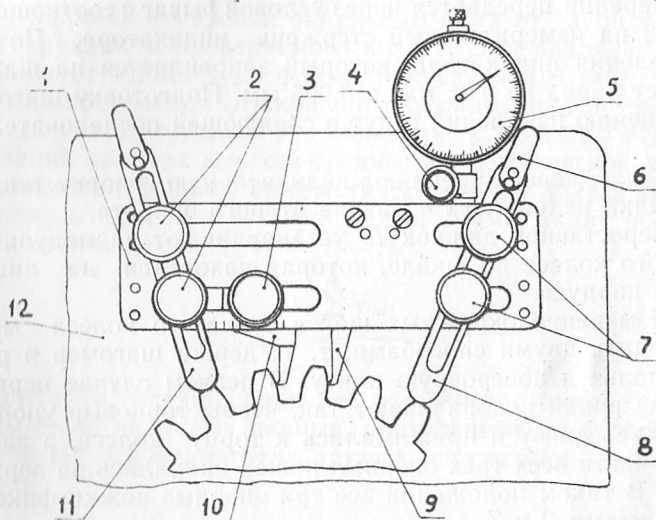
Накладной шагомер для проверки окружного шага зубчатых колес.
